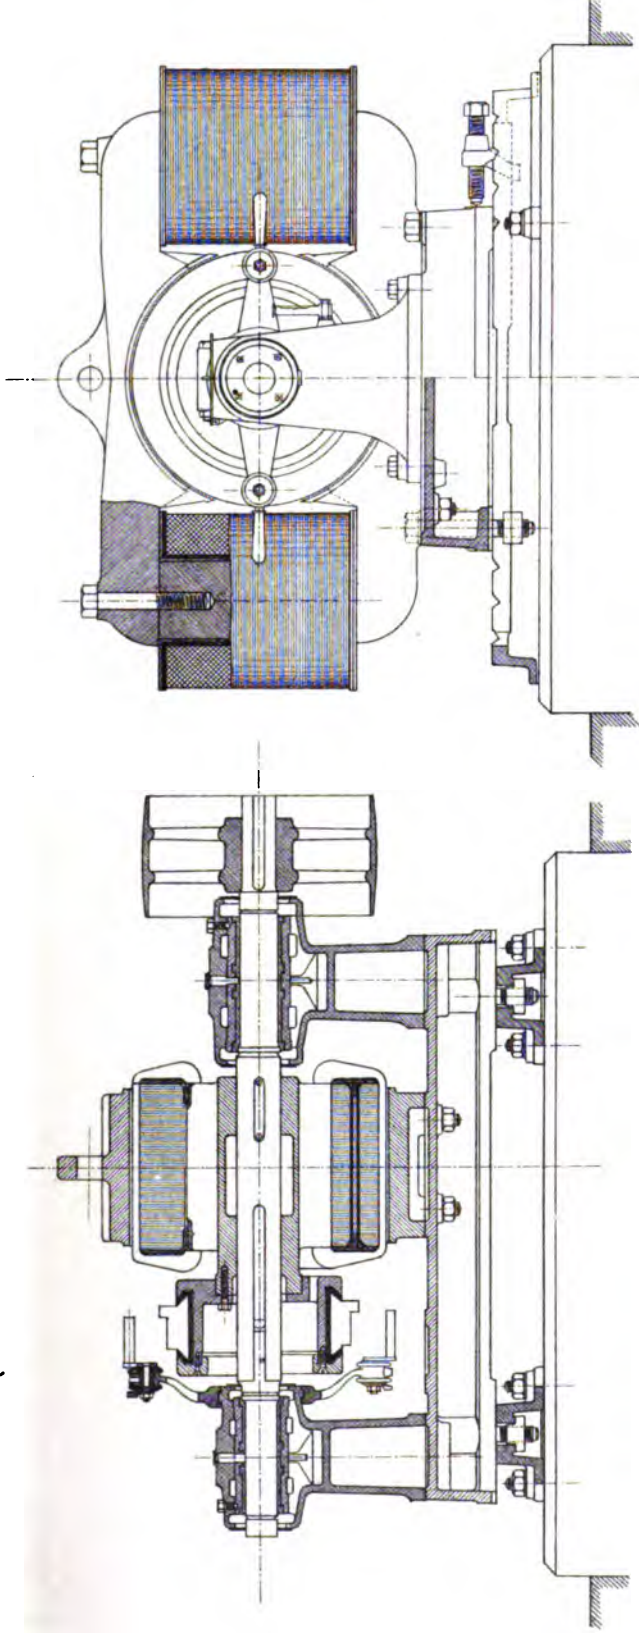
Zweipoliger Motor mit Zahnradvorlage von Schuckert & Co.
